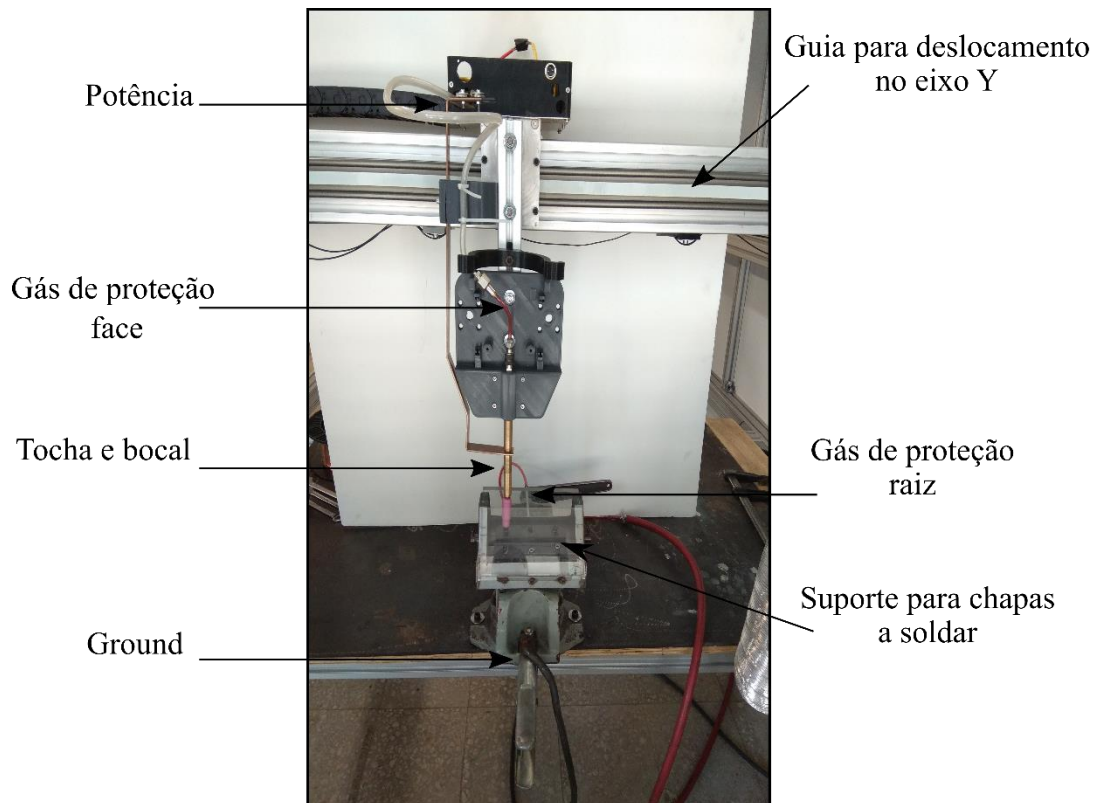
Tocha de soldadura TIG utilizada.
